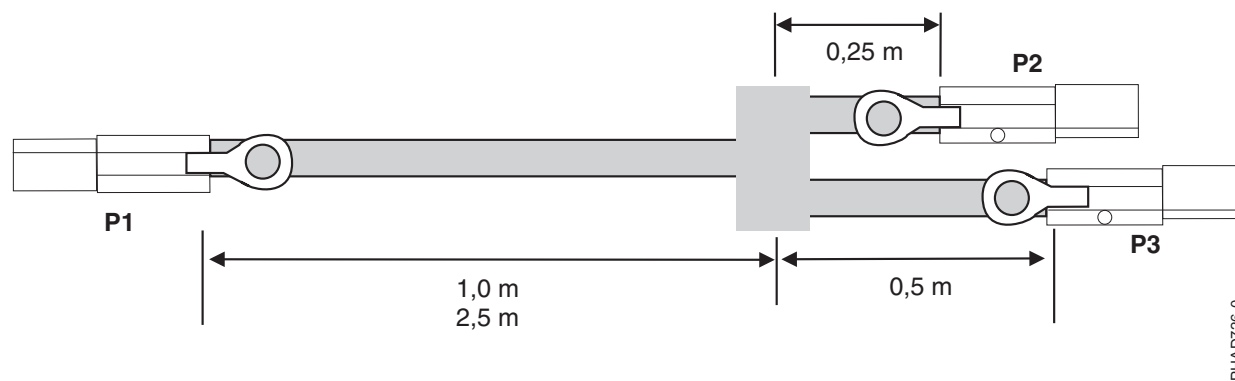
Longituds de cables de conjunt de cable YI SAS extern
